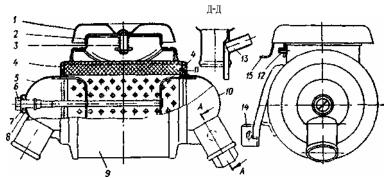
Воздушный фильтр с бумажным филырующим элементом: І - крышка; 2 - воздушная заслонка; 3 - пружина воздушной заслонки; 4 - прокладка; 5 - левая крышка фильтра; 6 - специальный болт; 7 - шайба; 8 - прокладка; 9 - корпус фильтра; 10 - правая крышка фильтра; 11 - фильтрующий элемент; 12 - ш гиф г фиксатора крышки; 13 - патрубок для присоединения крышки сапуна; 14 - кронштейн крепления фильтра; 15 - ручка управления воздушной заслонкой
